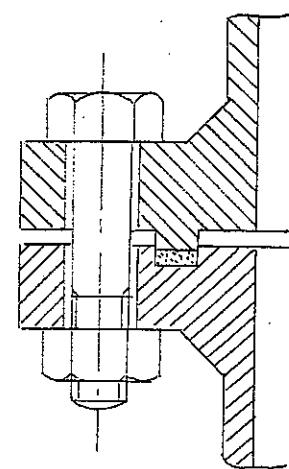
Вид С/Д обработки торцев фланцев со шпунтовой и шлицевой прокладкой
